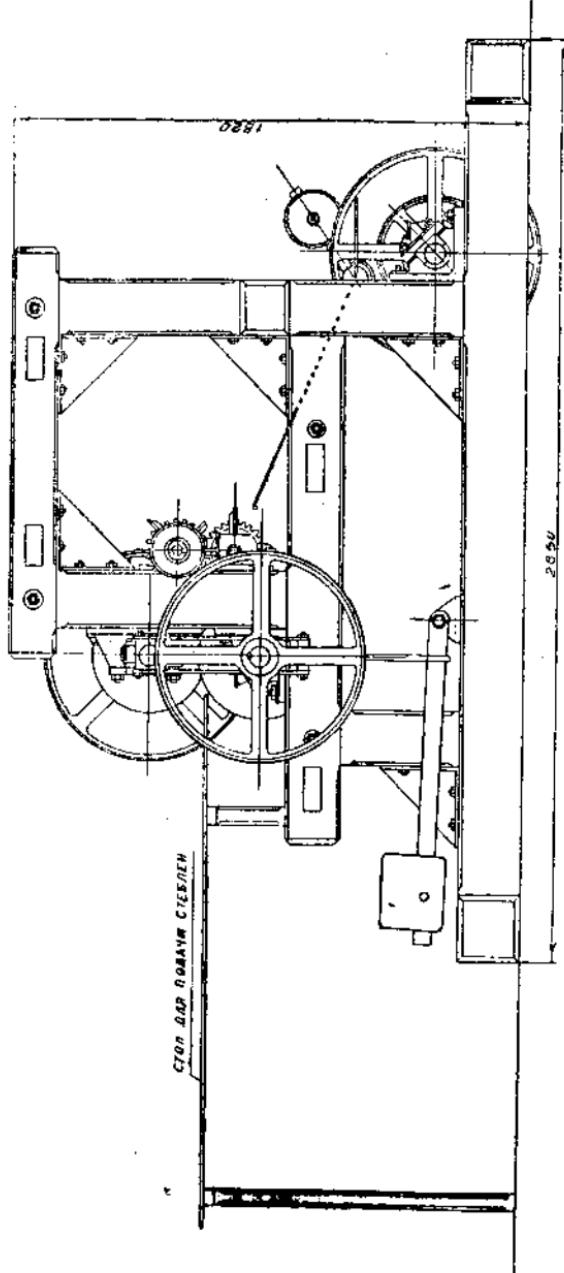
Дискретикатор Петрова и Барбасина. (вид сбоку).
